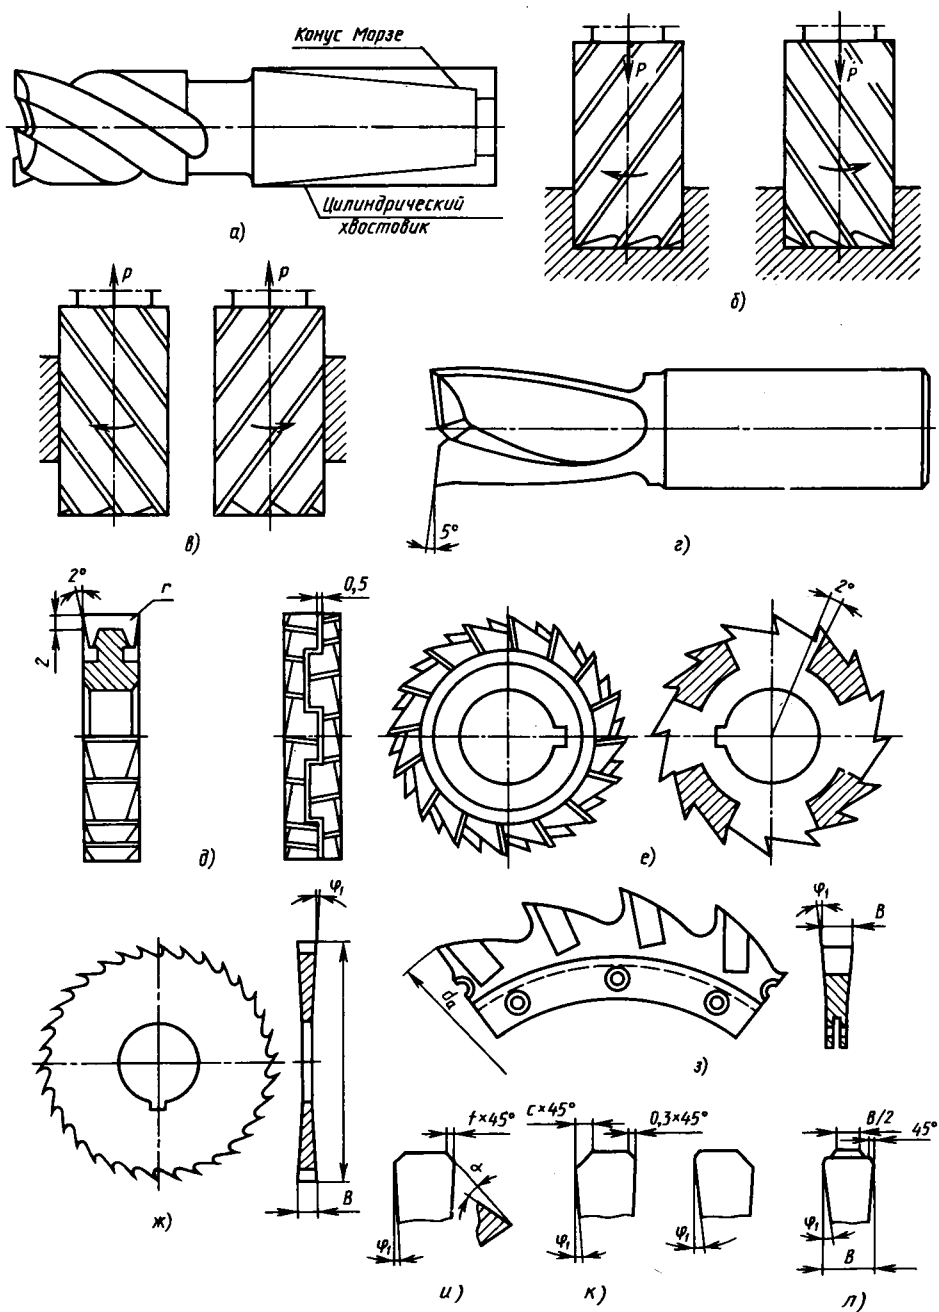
Цельные фрезы из быстрорежущей стали
